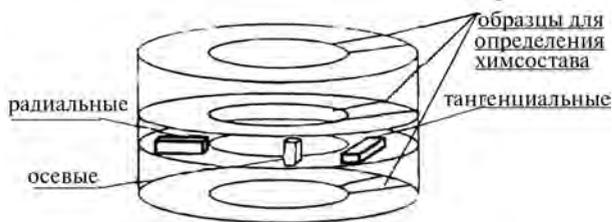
Схема вырезки образцов из электрошлаковой заготовки
